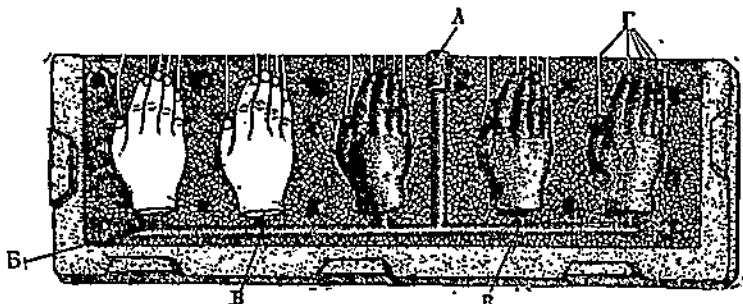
Отливка „под давлением“. Форма для одновременной отливки нескольких экземпляров. Передняя половина формы. А—литник. Б—общий канал. В—остротки канала. Г—воздушные каналы.
